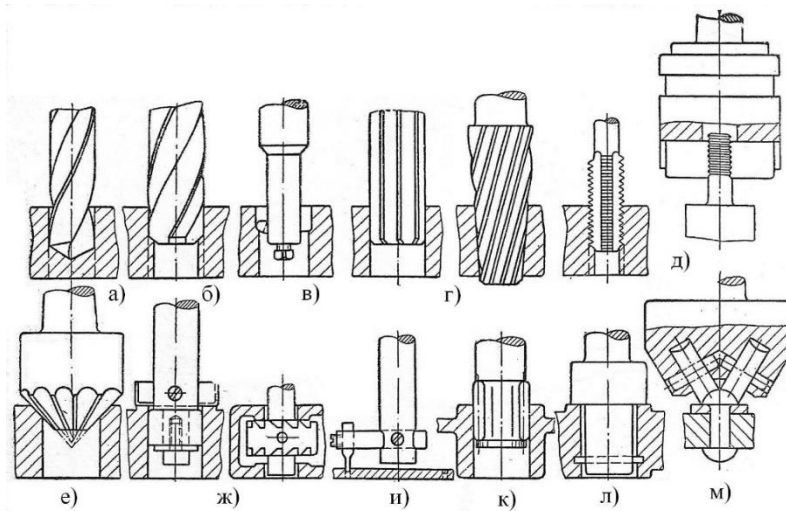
Схеми видів обробки на свердлильних верстатах
